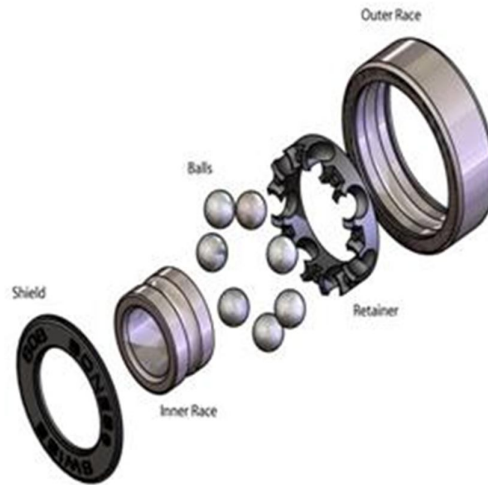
24.- Explosionado de un rodamiento rígido de una hilera de bolas.
